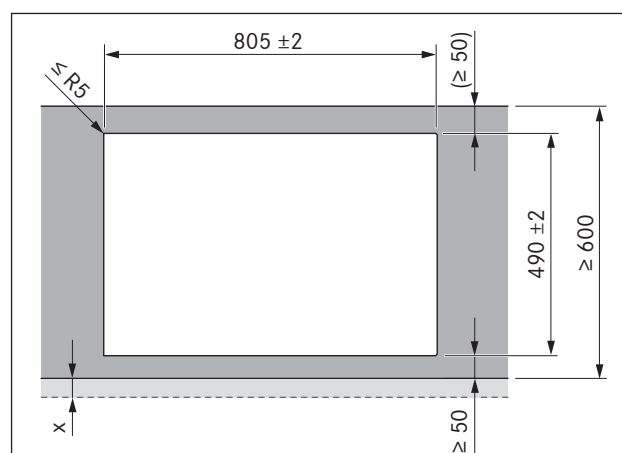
Dimensions de découpe pour montage par le dessus
